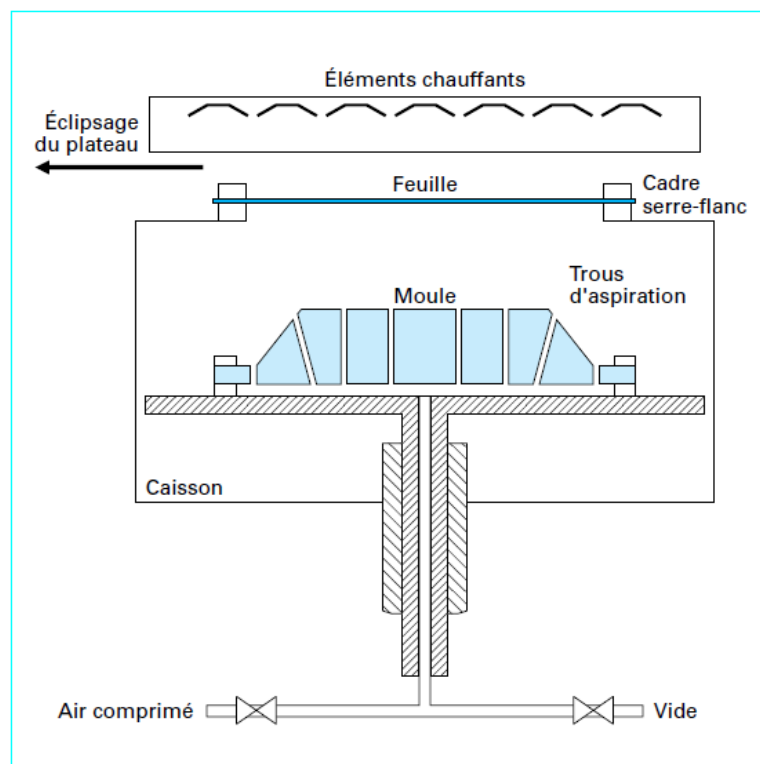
Schéma d'une machine de thermoformage à moule positif
